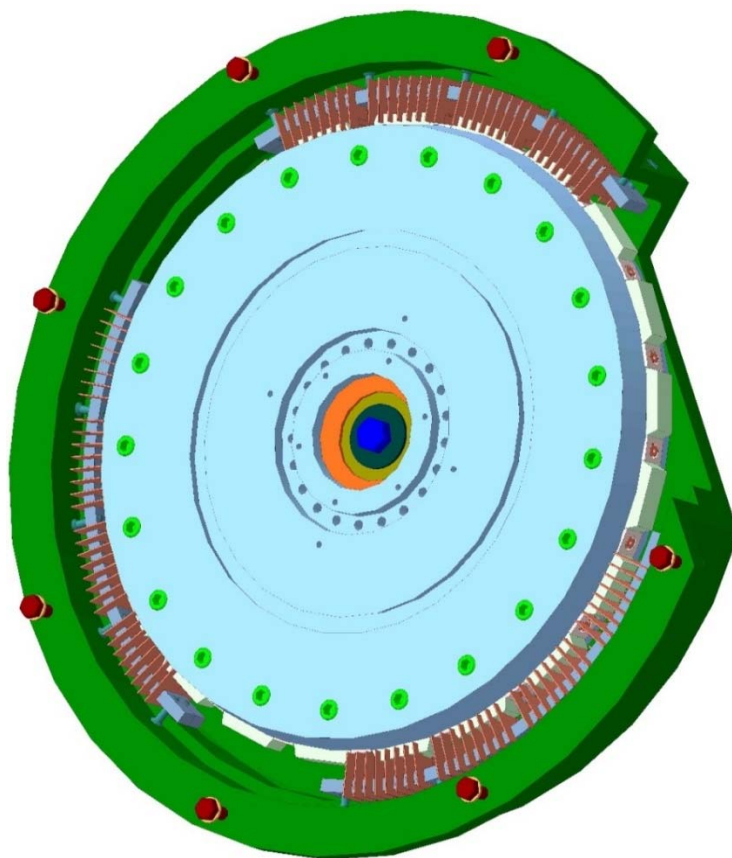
Установка элементов в кассете модуля сборного шлифовального круга.
